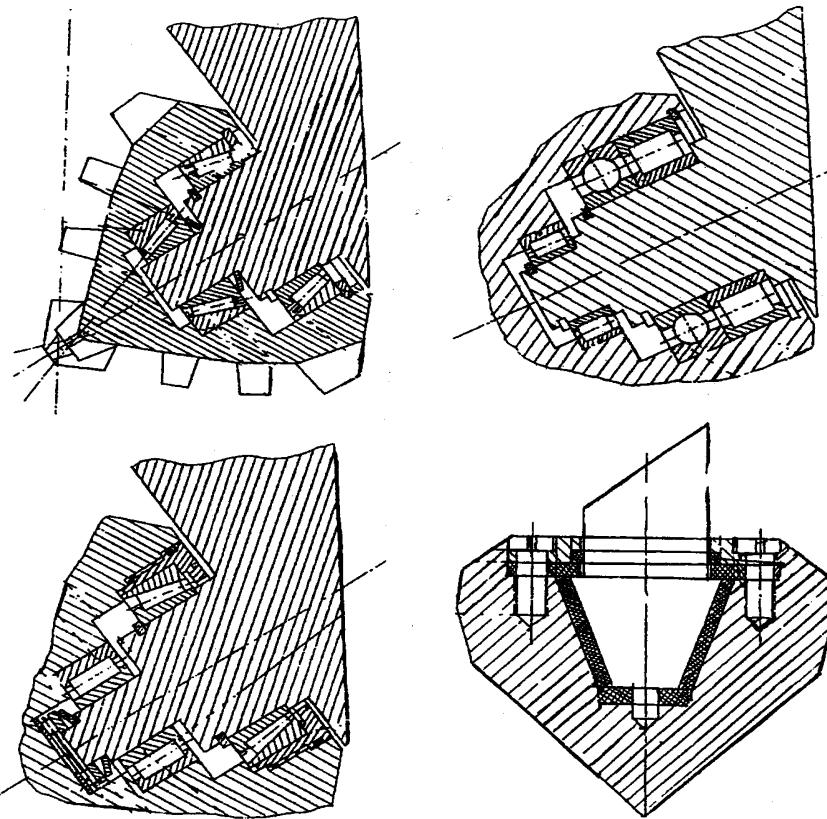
Разновидности опор шарошек с различным расположением подшипников качения
